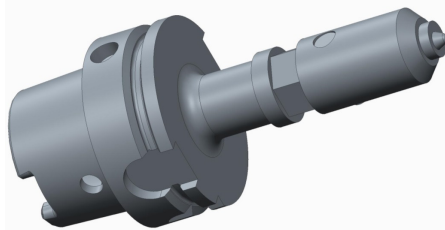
CAD-Modell Werkzeugprototyp zum 3-D-Rollieren
